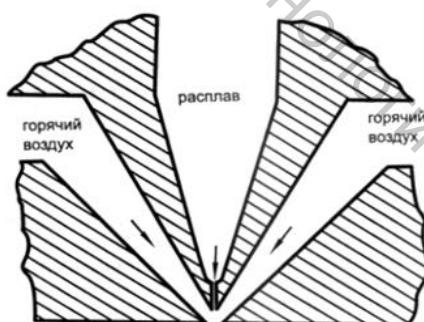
Поперечное сечение сопла для раздува расплава
